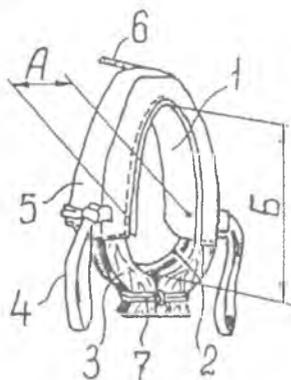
Хомут неразборный стандартный сельскохозяйственный: 1 - хомутная подкладка; 2 - хомутина; 3 - клещи; 4 - пара гужей; 5 - покрывка; 6 - горт; 7 - супонь
